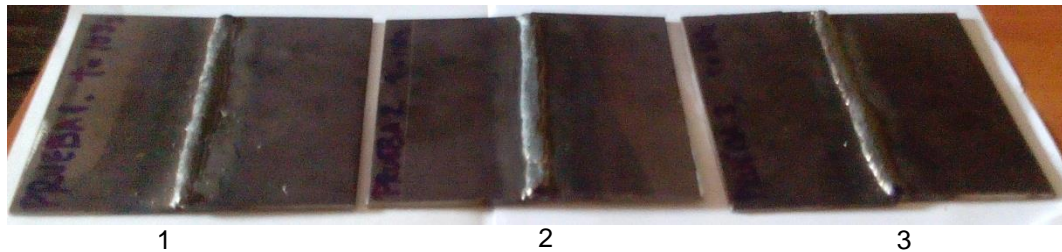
Juntas soldadas con placas de 76.4 mm de ancho.
